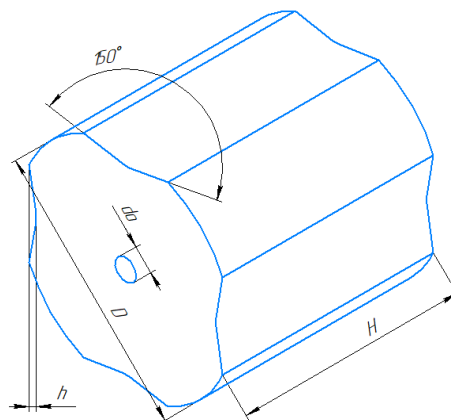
3D-модель профільованої заготовки на чотирипроменевий переріз
